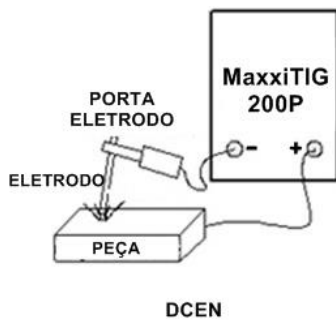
Conexão negativa para soldagem com eletrodo revestido
